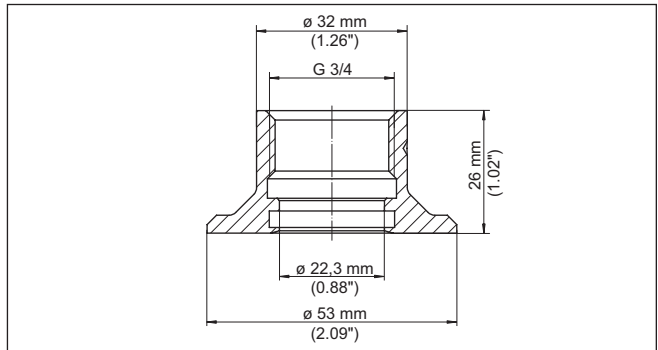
Medidas racor soldado G $\frac{3}{4}$ (ISO 228-1)
